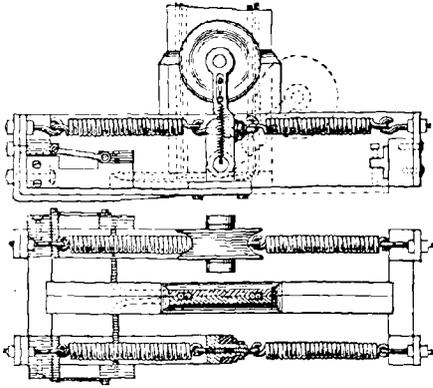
Trolley du caniveau de la 3^e Avenue de New-York.
